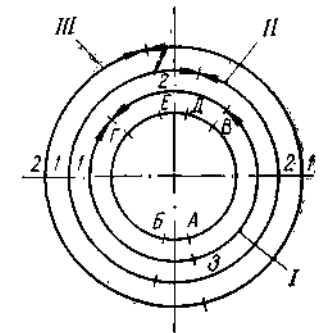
Сварка неповоротных (потолочных) стыков. I — первый слой; II — второй слой; III — третий слой. Стрелками показано направление движения дуги, цифрами — последовательность наложения шва.
